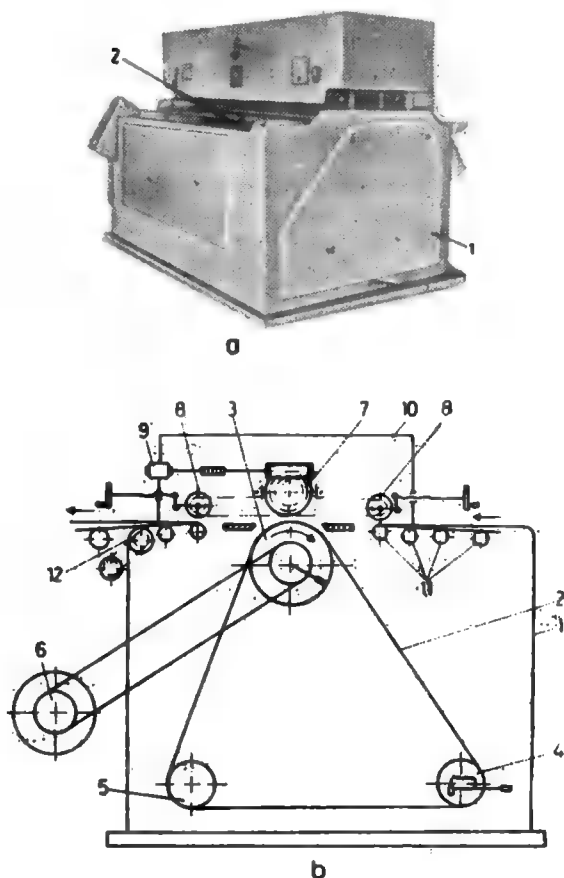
Mașina de șlefuit cu contact de jos :
